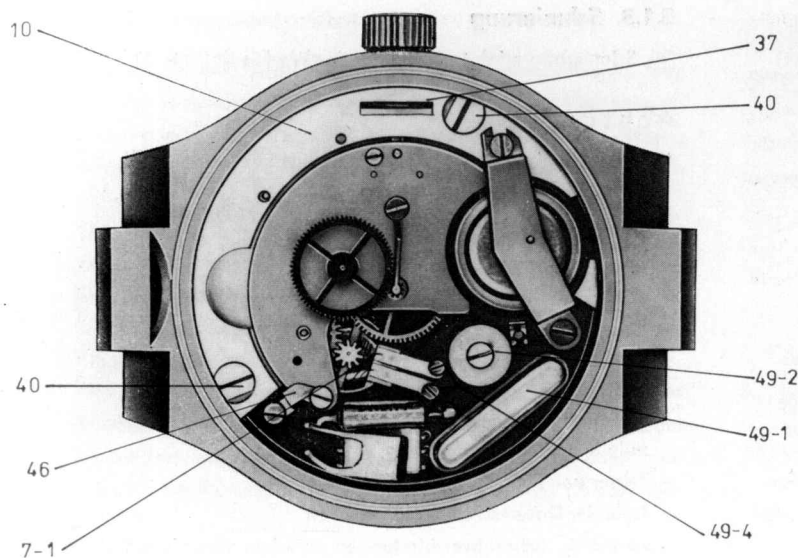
Rückansicht des Werkes 28-40 Ausf. II
